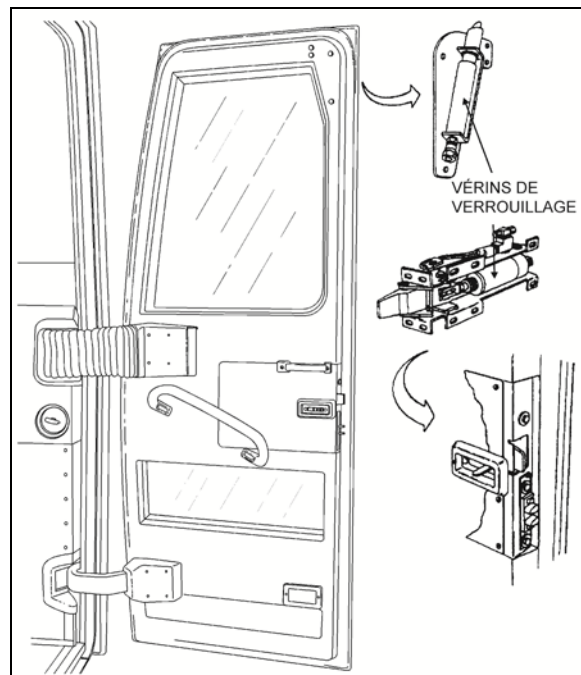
PORTE D'ENTRÉE D'AUTOCAR
